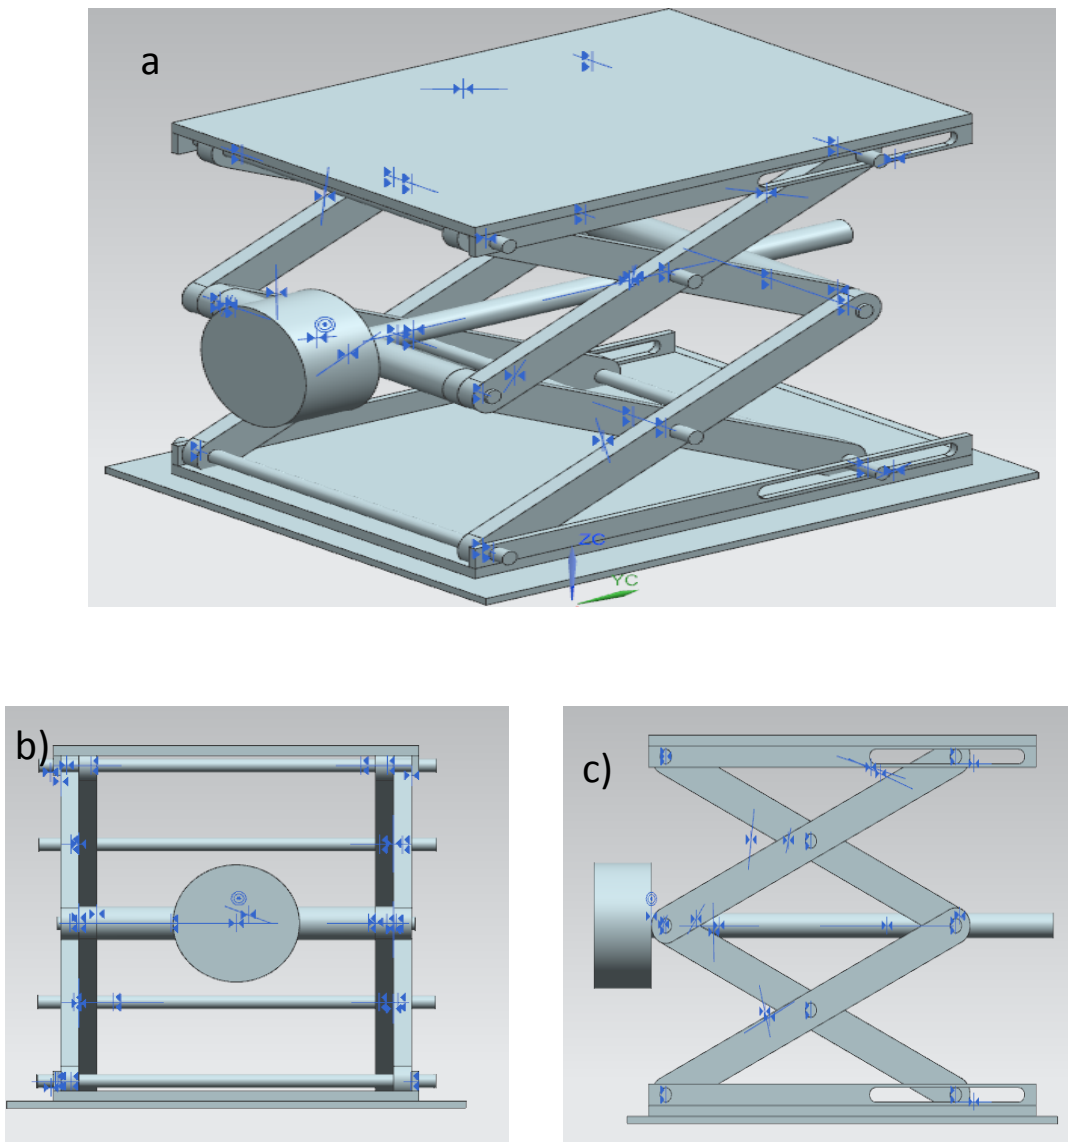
a) Ensamble final del gato mecánico propuesto, vista isométrica. b) Vista lateral izquierda, c) vista frontal.
